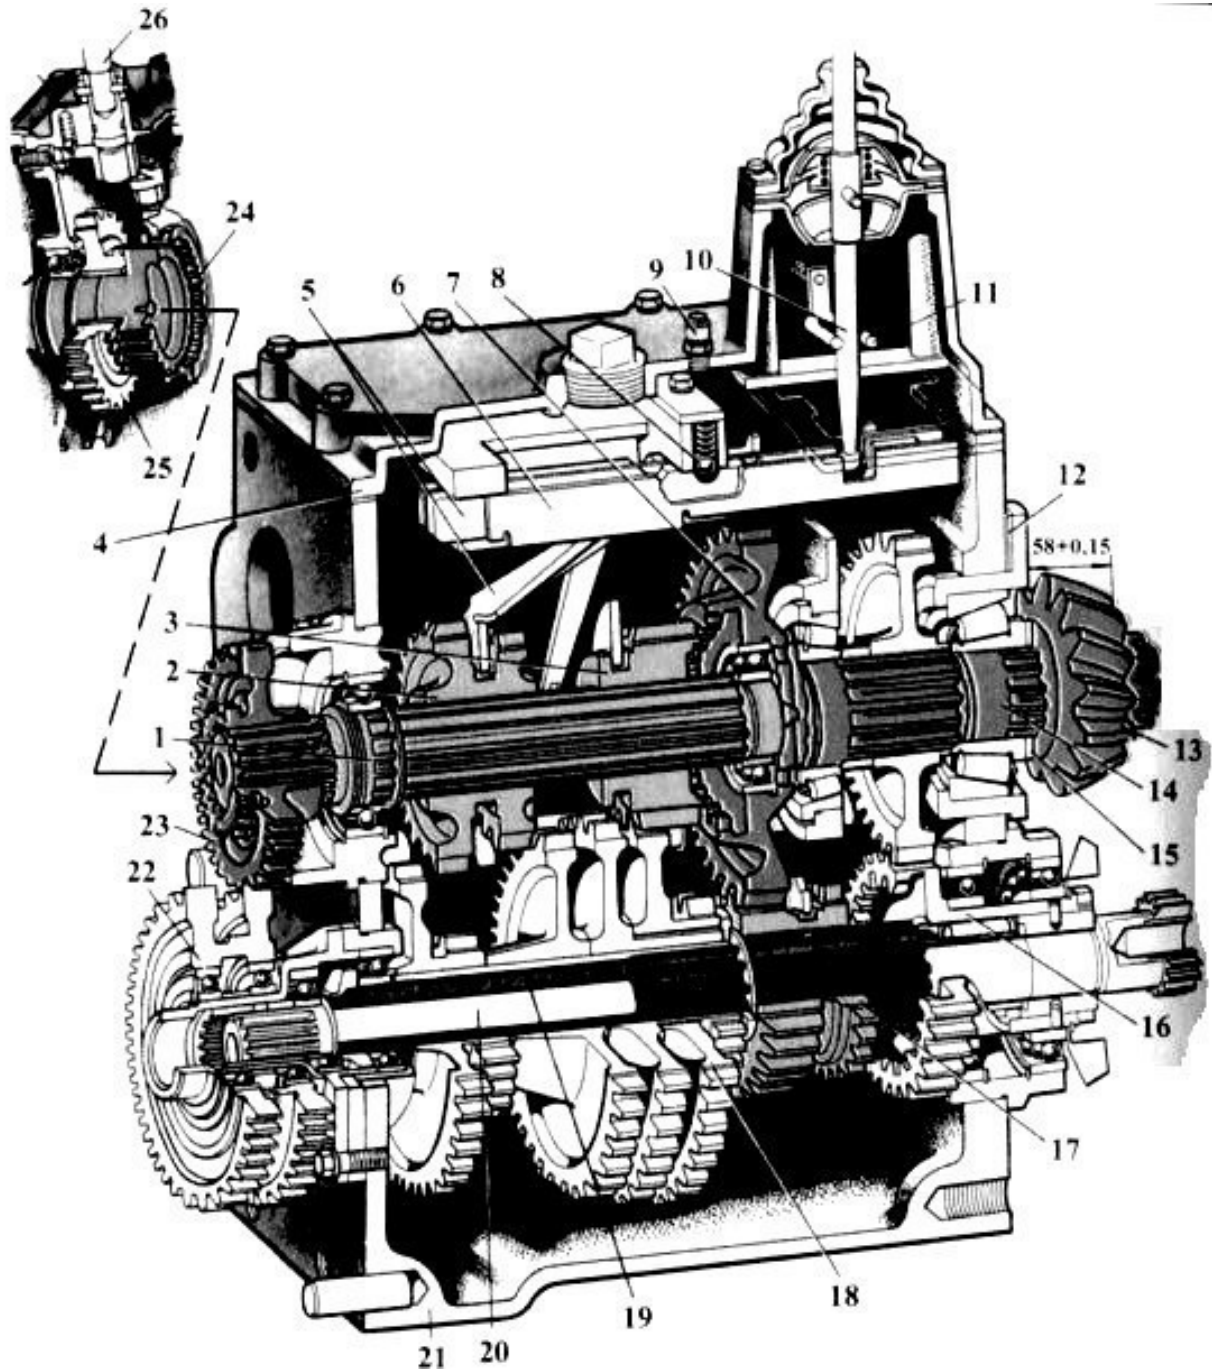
Коробка передач с подвижными шестернями трактора МТЗ-80
